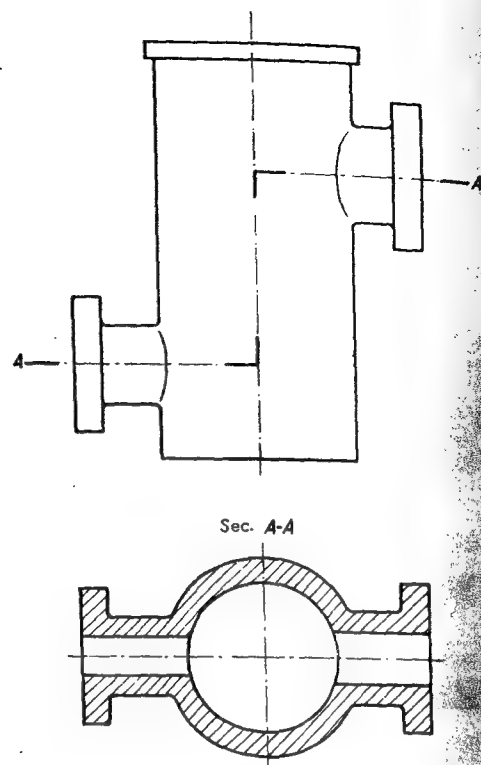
La sección A-A se ha hecho según dos planos paralelos y se ha colocado en el sitio de la planta (vista por encima), de la que tiene el mismo contorno. Aquí también se han dibujado con línea más gruesa las trazas de la intersección de los planos cortantes.
